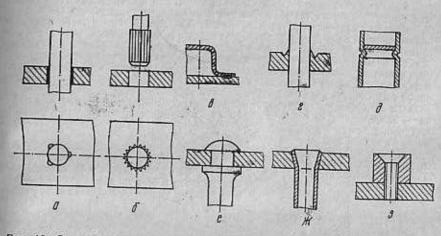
Способы закрепления элементов изделия при сборке и пайке: a — кермение в трех точках;  $\delta$  — накатка; a — точечная сварка; a — кермение по контуру;  $\theta$  — знговка;  $\epsilon$  — расклепывание;  $\infty$  — развальцовка; s — крепление винтом.
